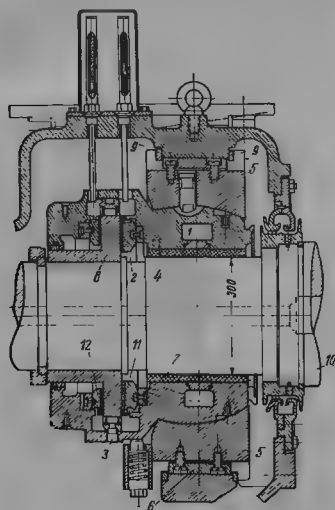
Комбинированный опорно-упорный подшипник ЛМЗ.
